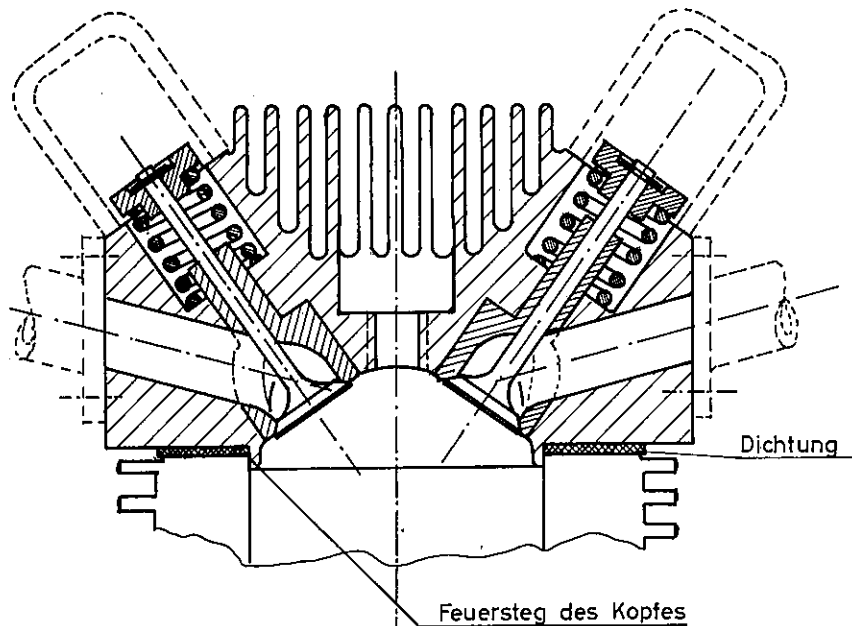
Zylinderkopf mit schräg hängenden Ventilen
